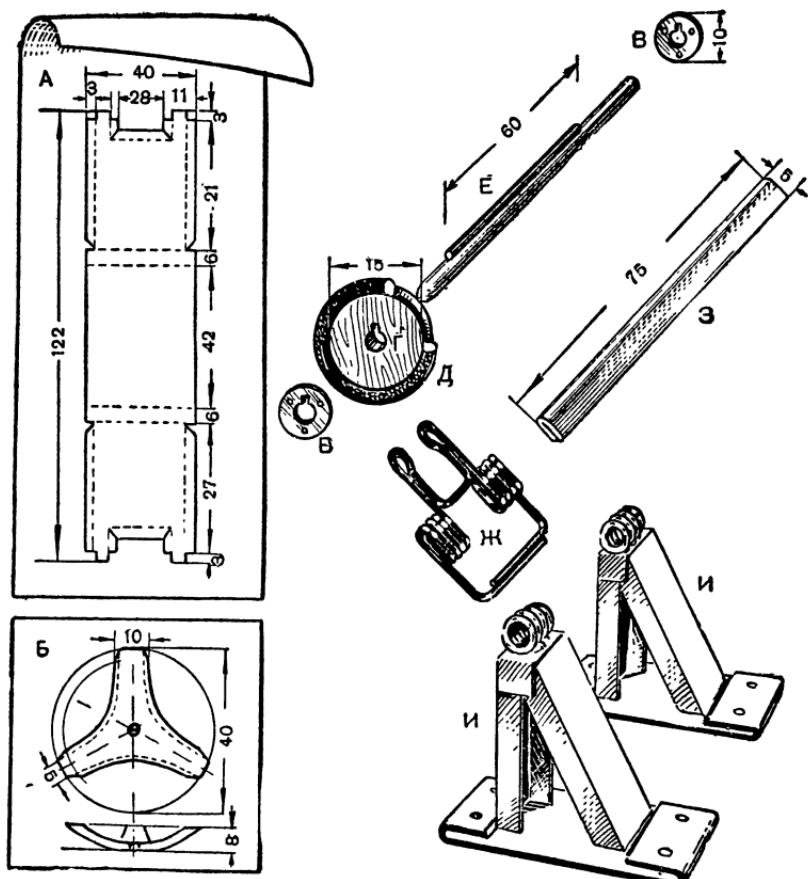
Детали редуктора № 4 (рис. 114): А — развертка стойки диска; Б — развертка «паука»; В — шайбы для ролика, Г — фрикционный ролик; Д — резиновое колечко; Е — вал ролика с припаянной проволокой; Ж — вилка; З — направляющая рейка; И — стойки ролика с подшипниками.
